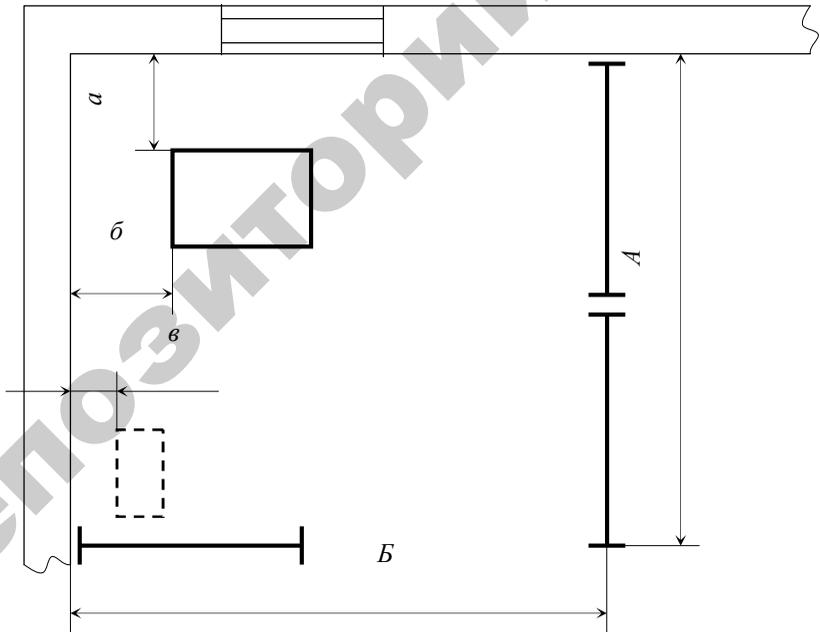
Нормы расстановки оборудования на сварочном участке
